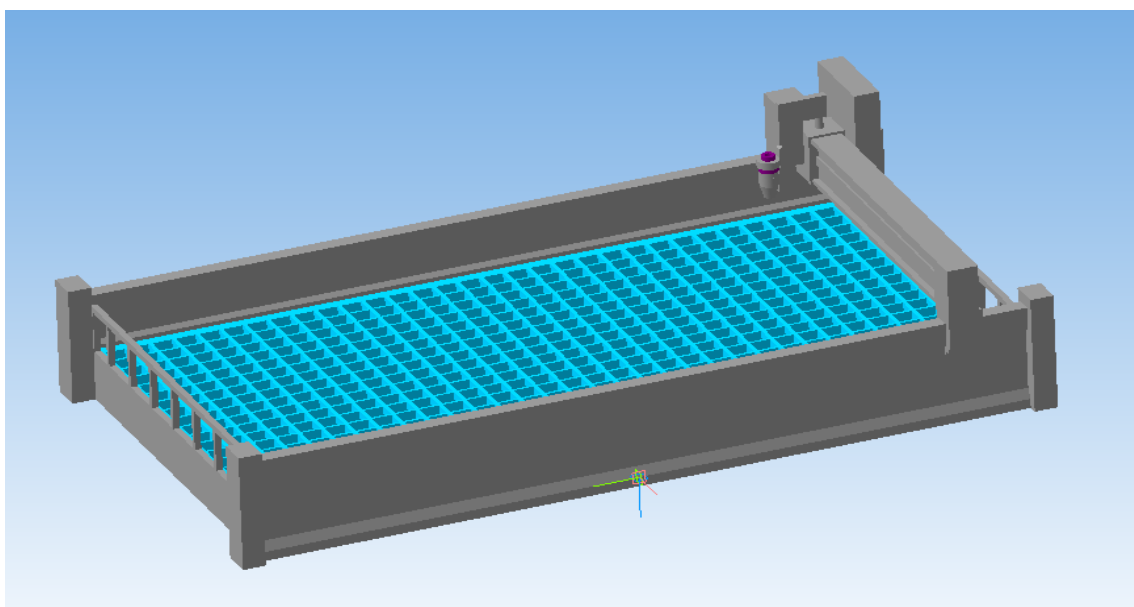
3D-модель стола установки для гидроабразивной резки
